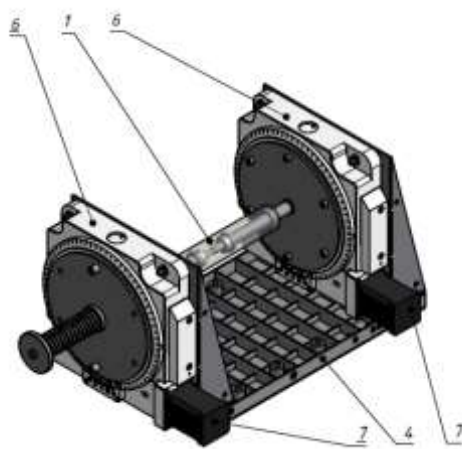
Система закрепления образцов для установки электронно-лучевой сварки стекла
